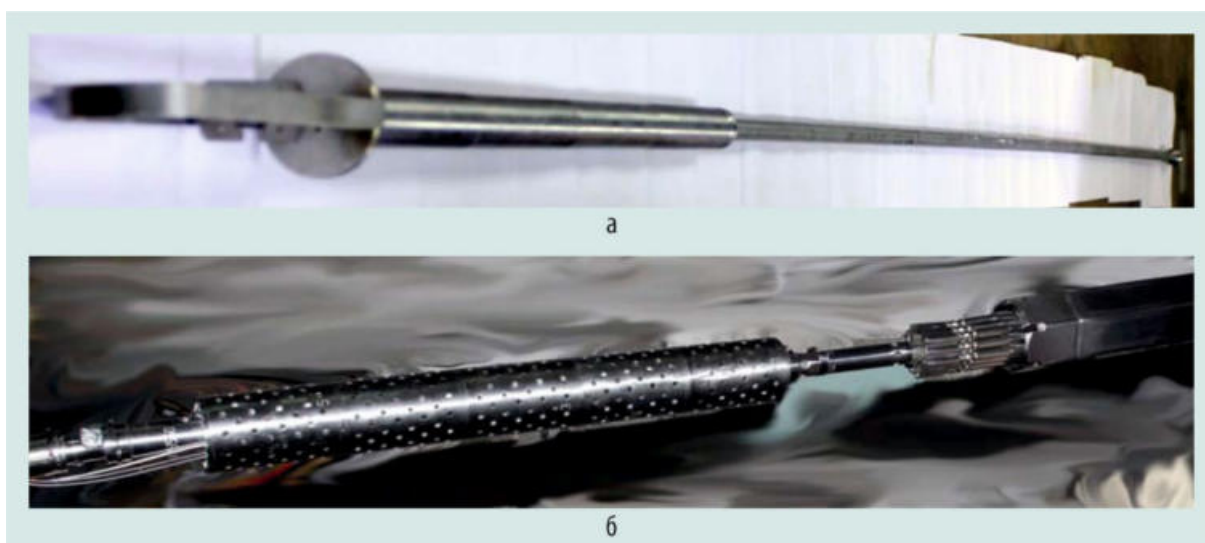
Внешний вид термозонда (а) и облучательного устройства после финальной сборки перед постановкой в реактор (б)
